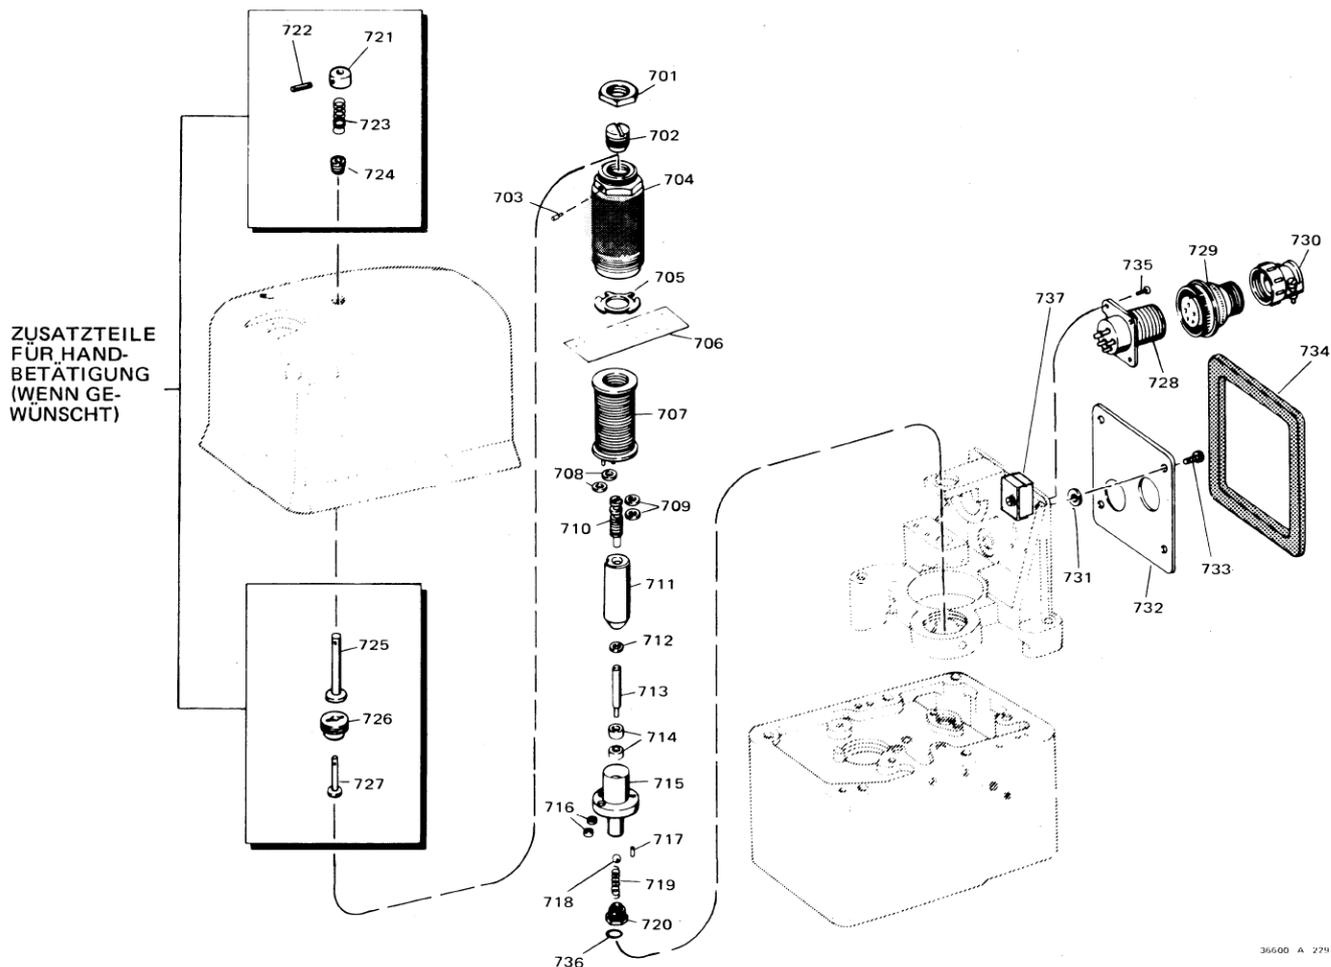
Explosionsdarstellung des Abstellmagneten
